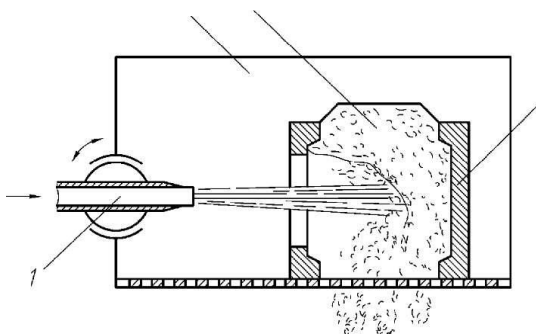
Схема удаления стержня из отливки в гидравлической камере:
